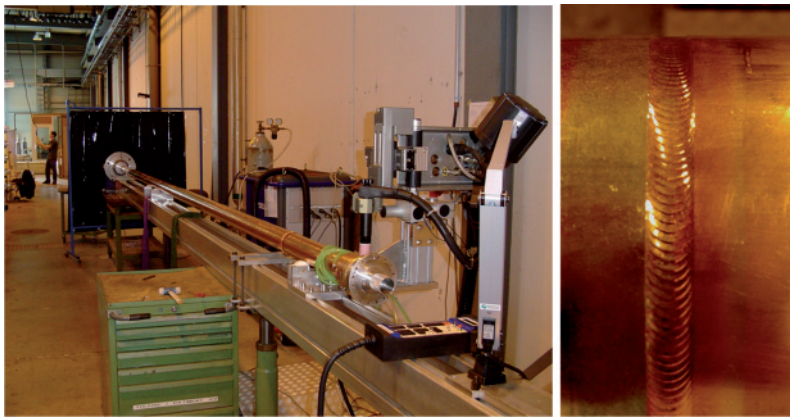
Links die Schweissanlage der LSS Kammern, Rechts die Schweissnaht OFS/OFE Kupfer
